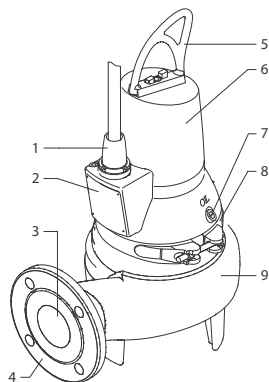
Pompe SL1.50.65 e SLV.65.65
